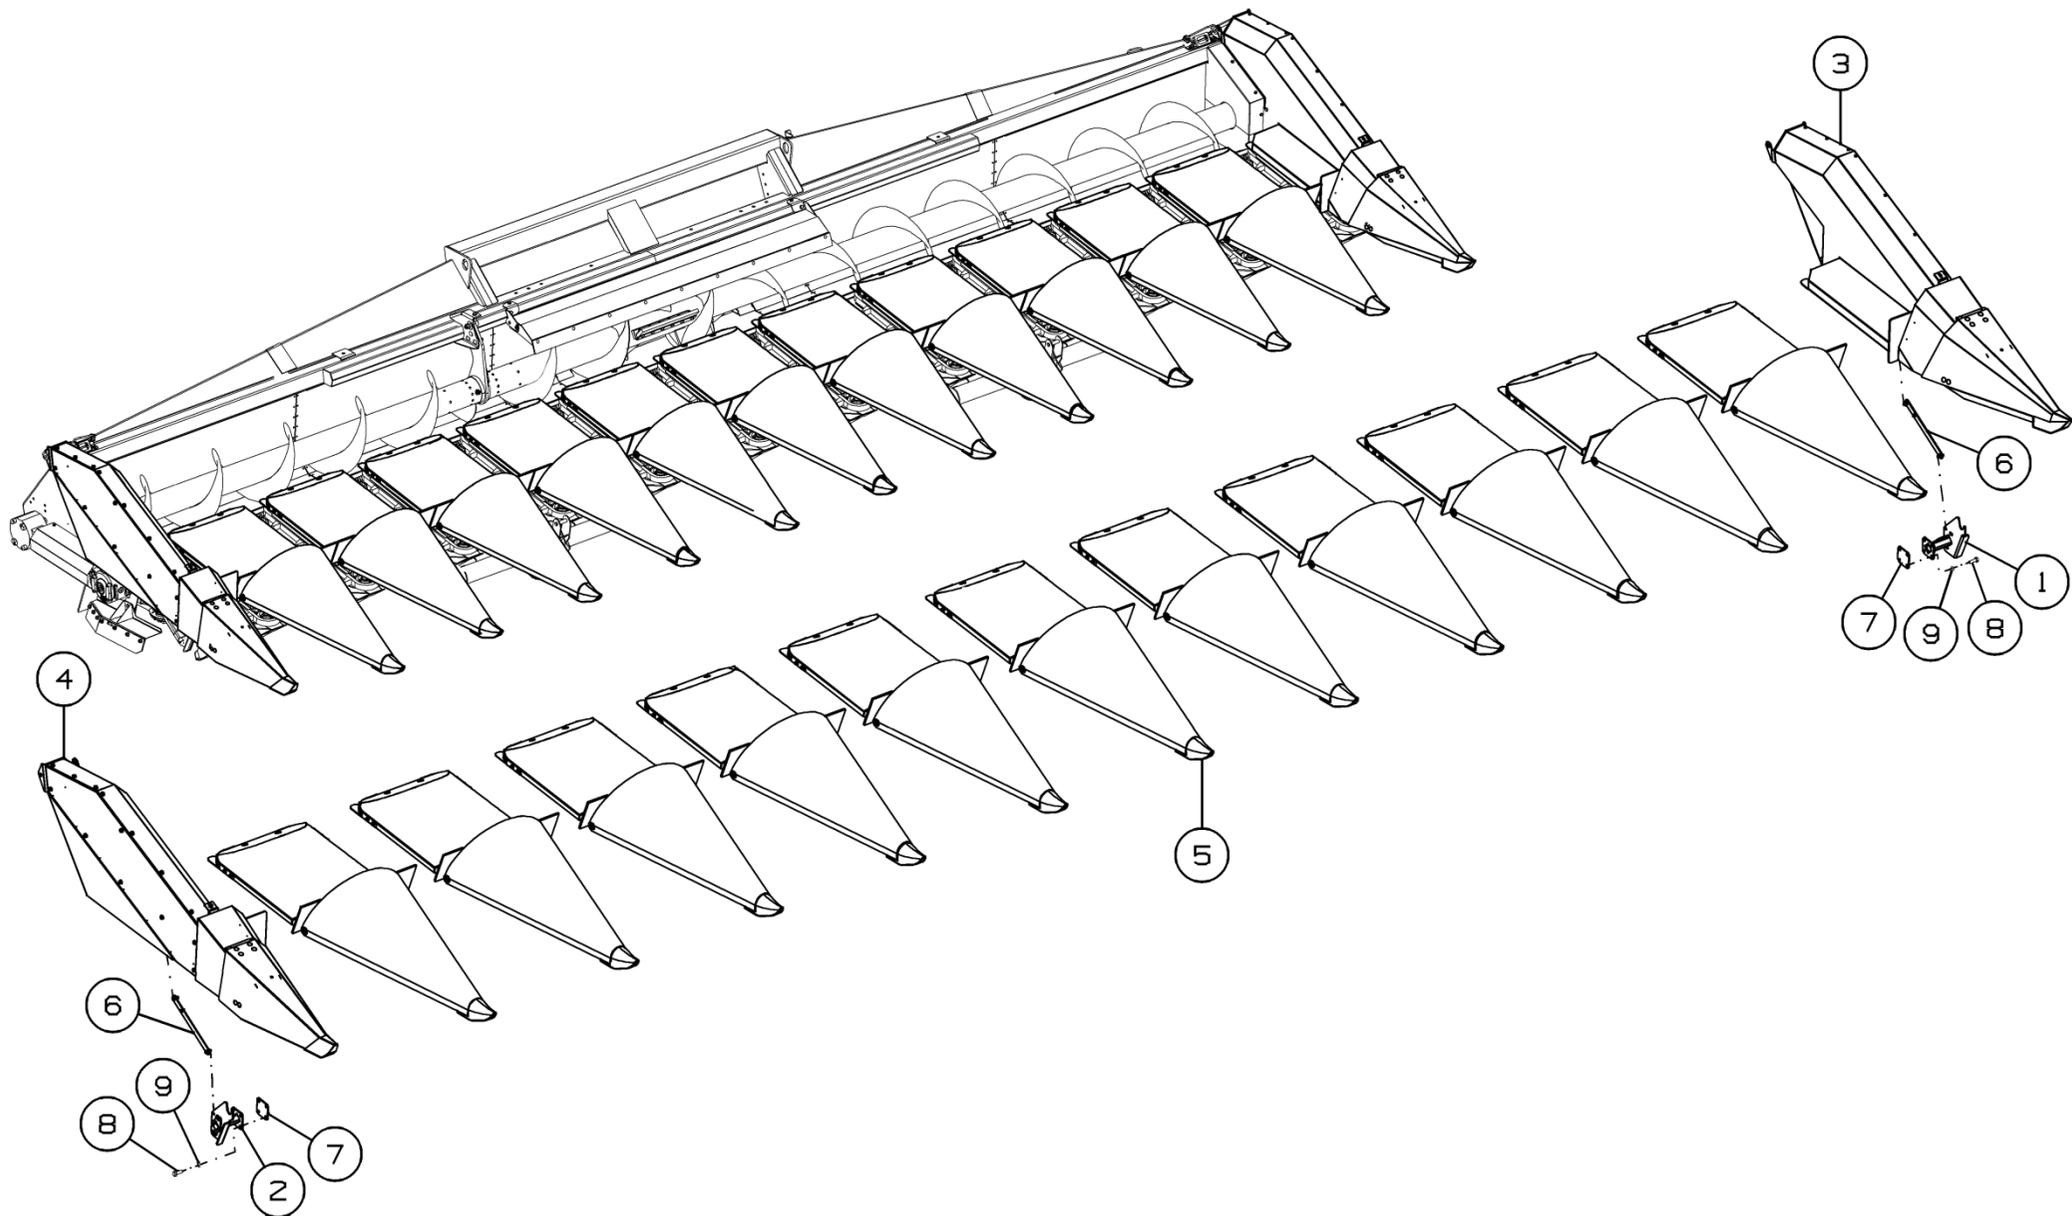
Установка капотов ППК-81.01.21.000-03
